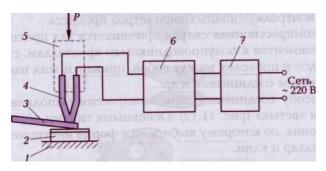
Устройство ультразвуковой сварки:
